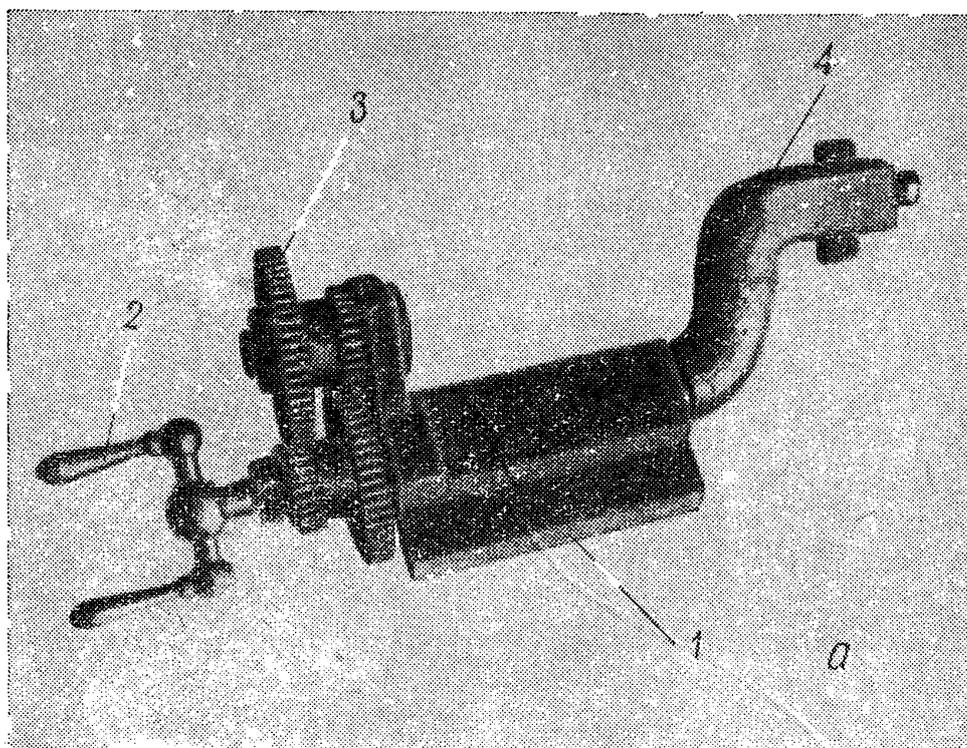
Обточка шаровой поверхности с помощью приспособления токаря В. А. Родионова:
